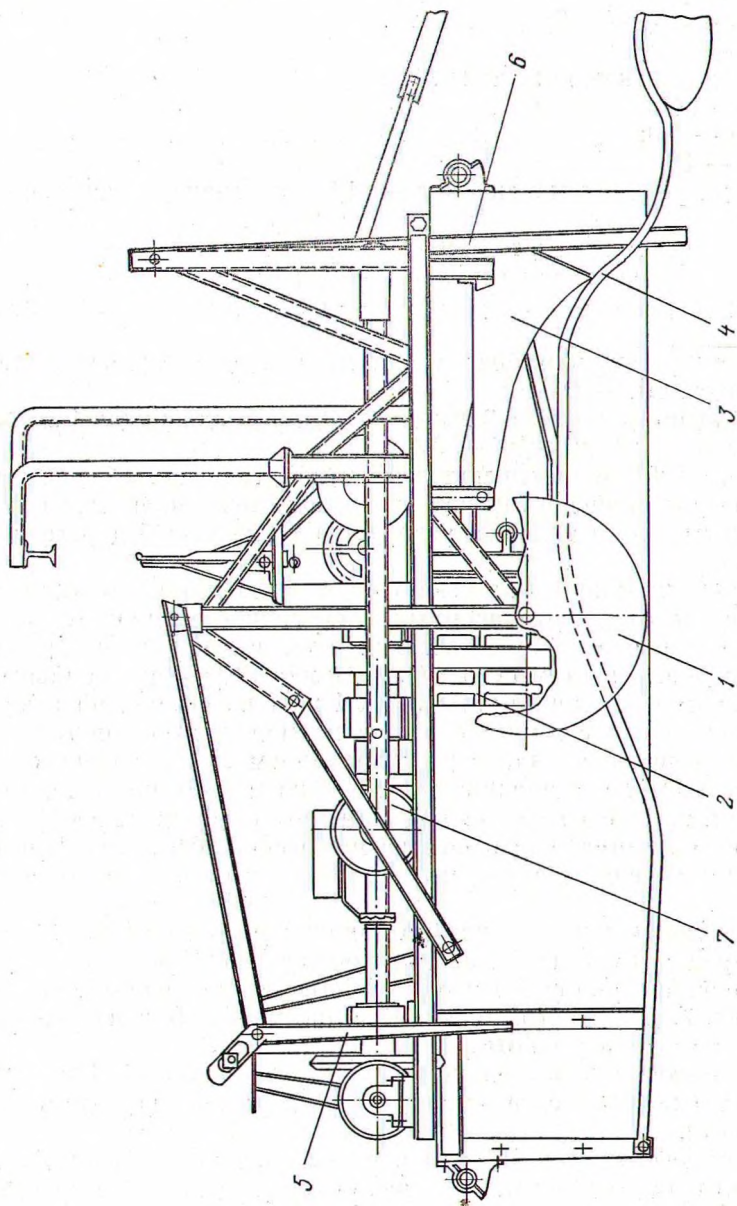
1 — отклоняющий диск; 2 — труба вращающего механизма; 3 — упор; 4 — направляющая поплавка; 5 — маятниковый рычаг; 6 — толкатель; 7 — коленчатый вал.
